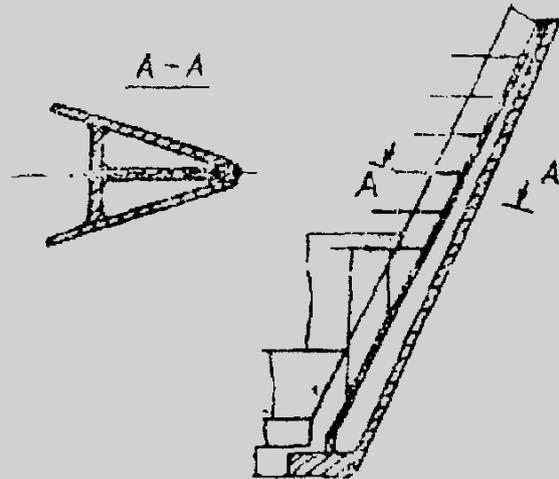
Форштевень сварной применением прокатного профиля
